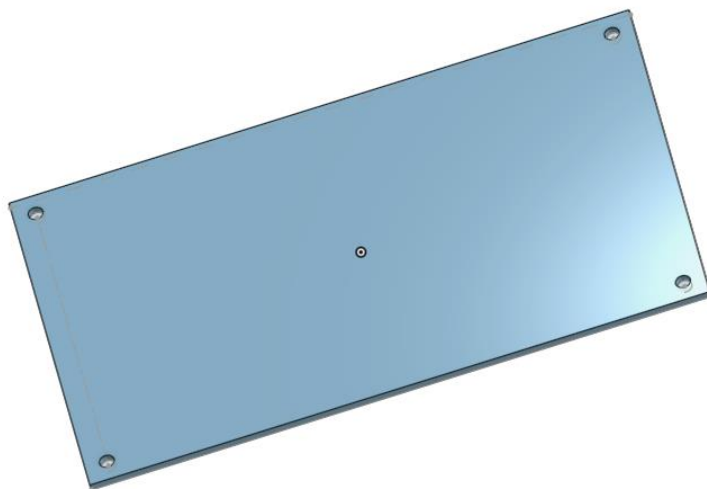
3D-модель кришки корпусу внутрішнього блоку
